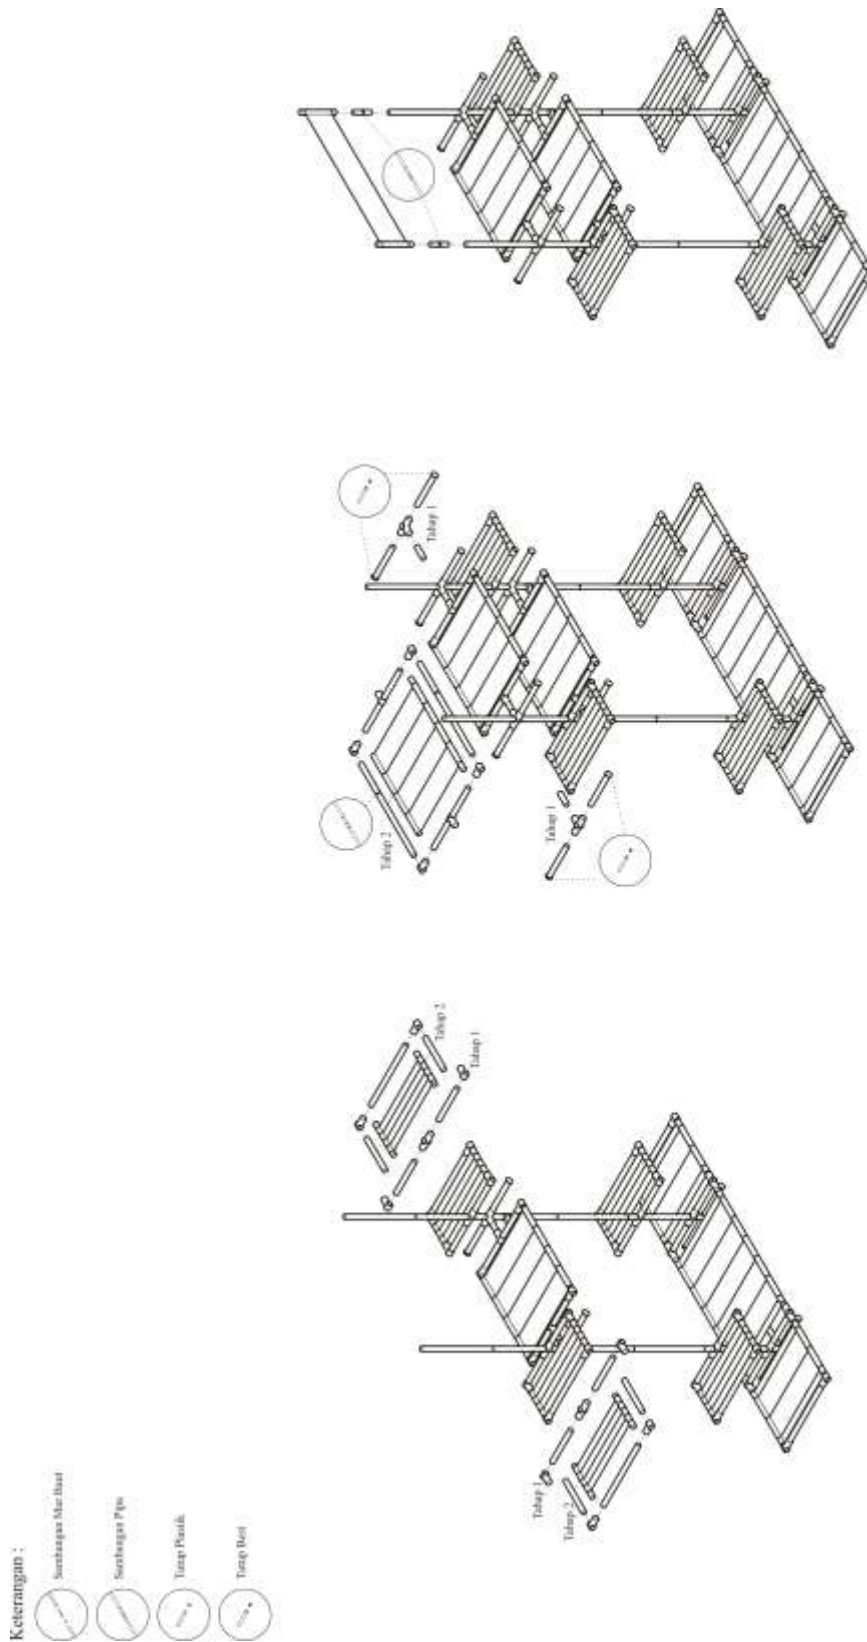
Detail Pipa, Kain dan Sambungan Modul 1
